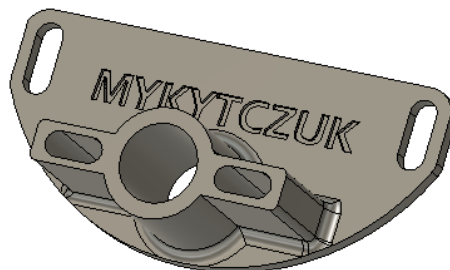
Projeto em CAD da Montagem final do Manicoto.
